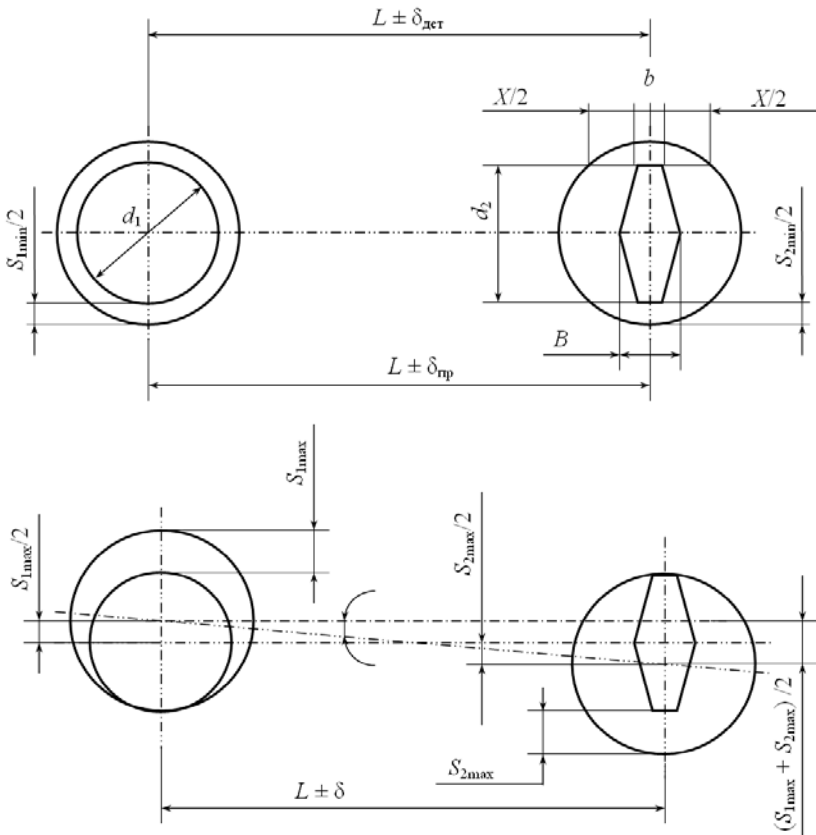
Схема установки обрабатываемой детали на два пальца и плоскость
